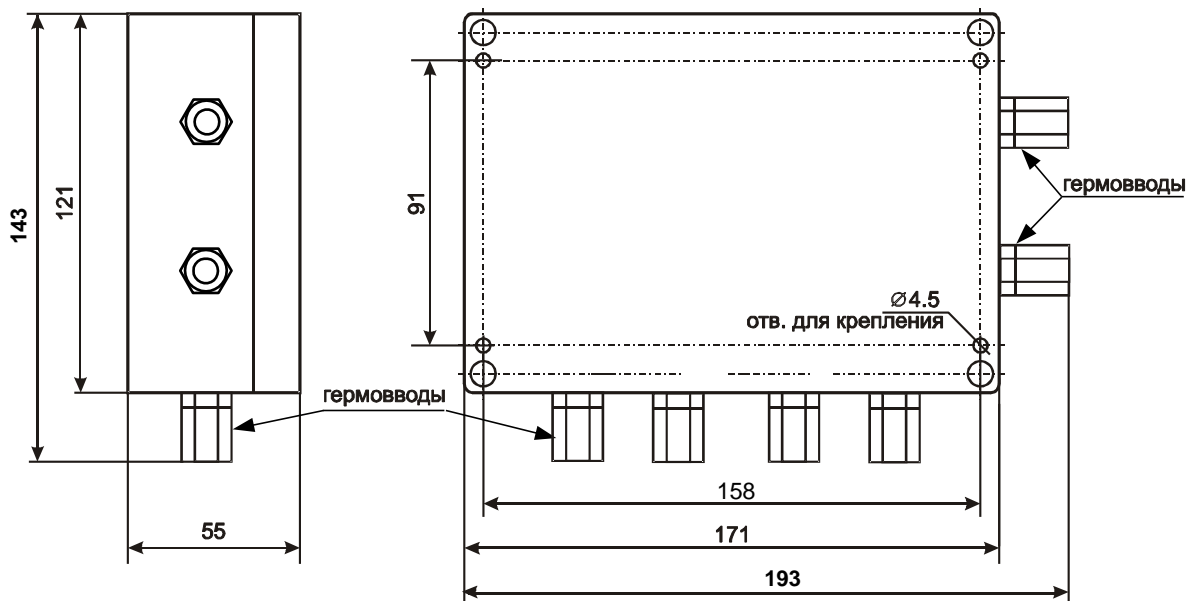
Габаритные и присоединительные размеры корпуса ИСМ220.4 исп.08К (IP65)
